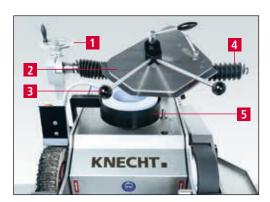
Универсальный шлифовальный рукав HV 203
